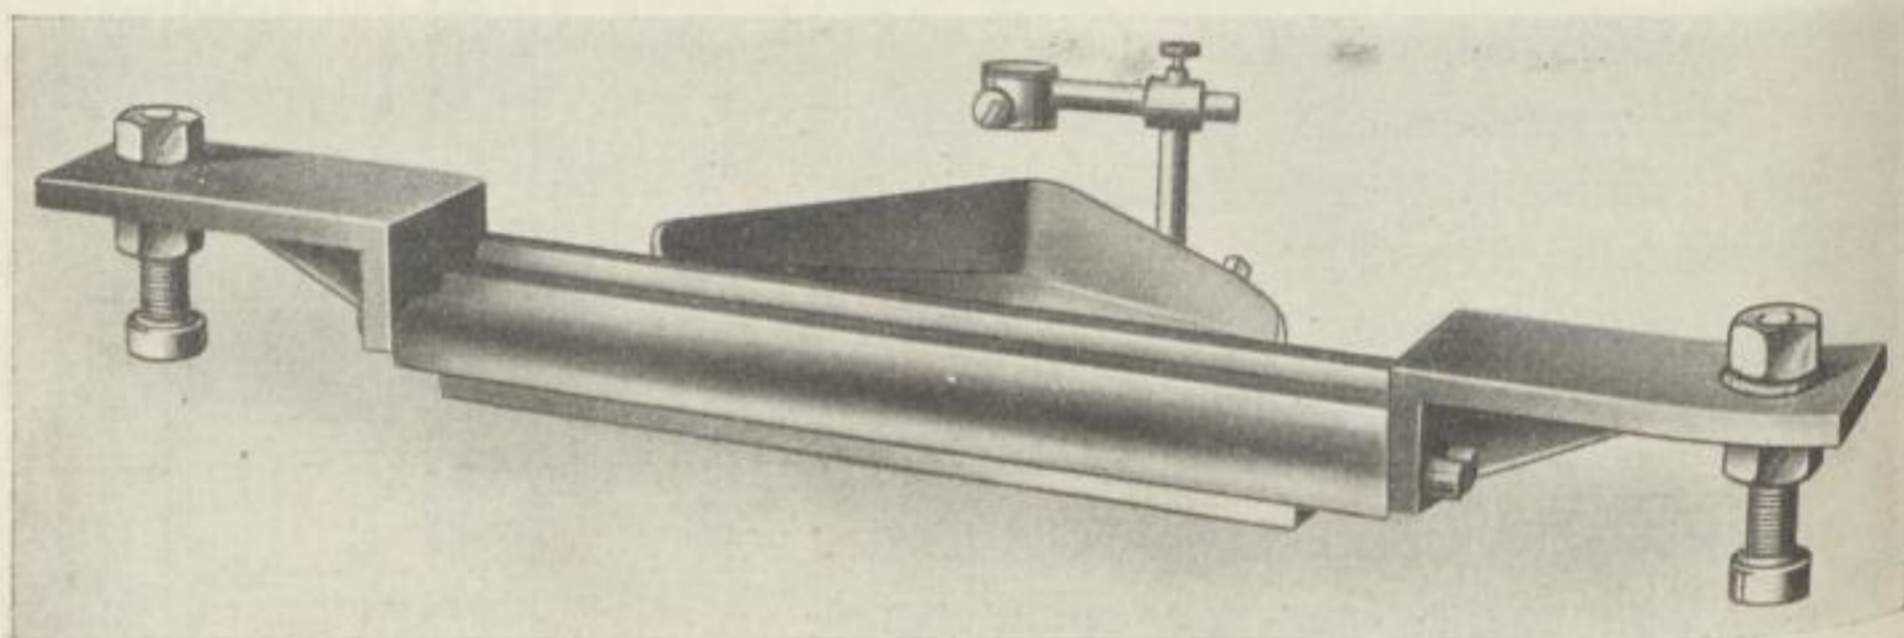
Kaskadengießer einer Trockenplatten-Begießmaschine.
